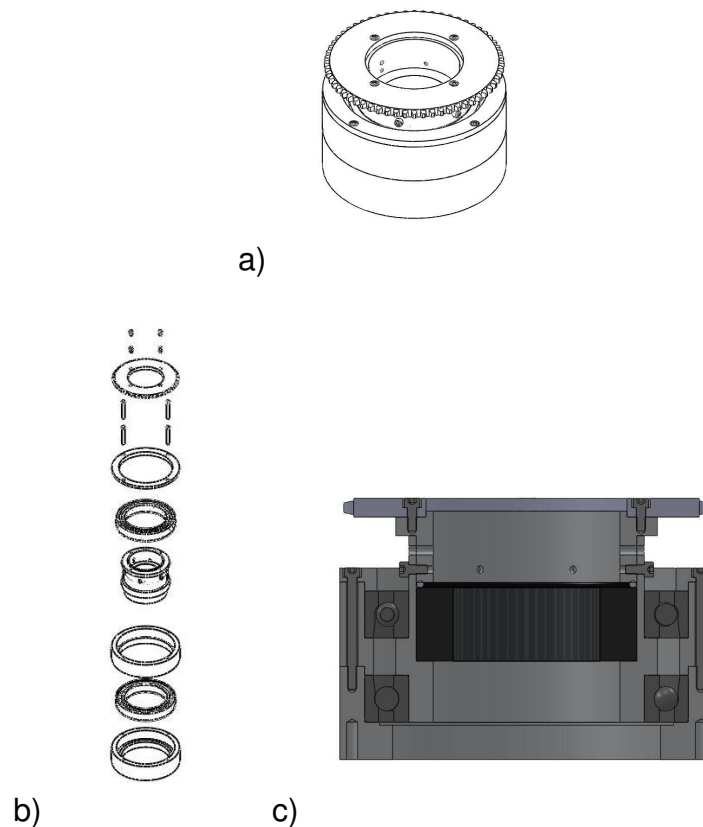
a) Subensamblado completo, b) Vista explosionada del subensamblado, c) Corte transversal del subensamblado del mecanismo del retardador.
